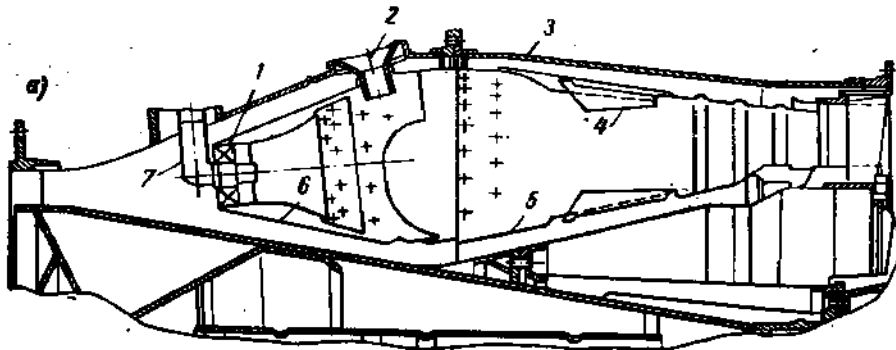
Кільцева камера згорання (двигун НК-12): 1 - завихритель потоку повітря; 2 - фіксатор жарової труби; 3 - зовнішній корпус; 4 - змішувач; 5 - кільцева жарова труба; 6 – фронтів пристрій; 7 - форсунка
